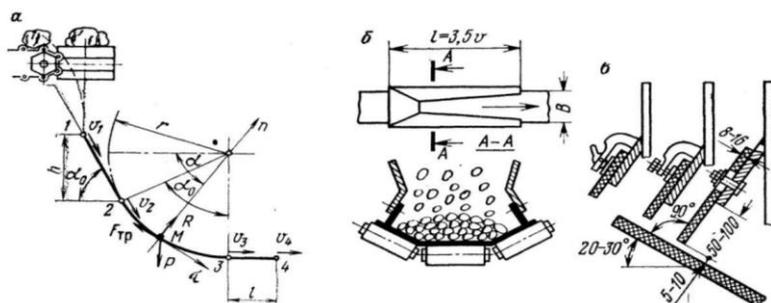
Конструкция загрузочного лотка: а - профиль лотка; б- направляющие борта; в - варианты установки нижней кромки бортов
